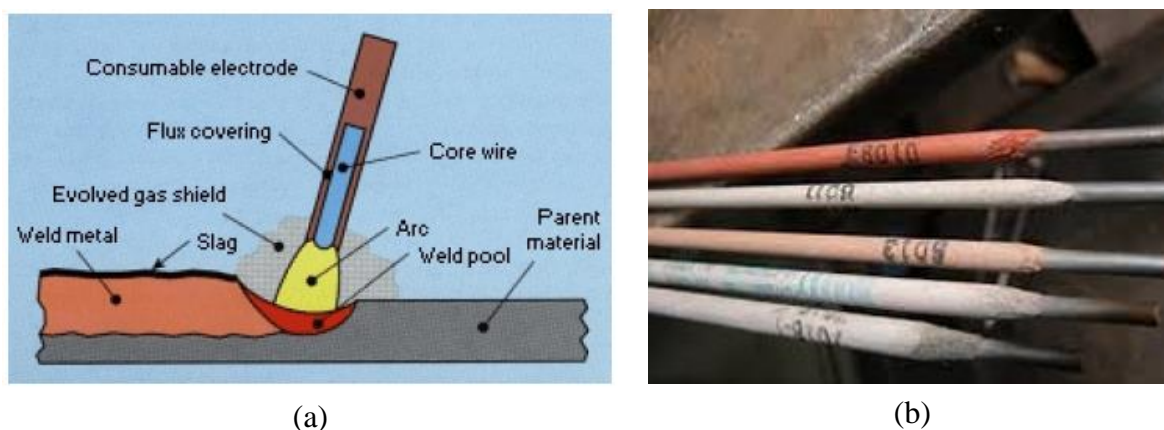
(a) Processo de soldagem a arco elétrico MMA [11]; (b) eletrodos de diferentes tipos e diâmetro.
